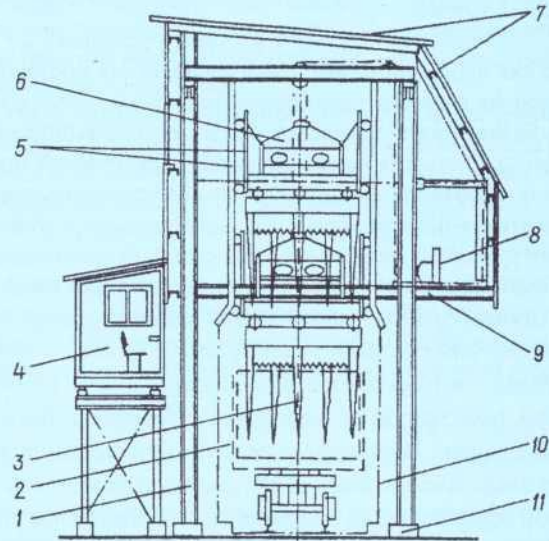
Общая схема виброрыхлительной установки: 1 — несущие балки; 2 — железнодорожный полувагон; 3 — рабочий орган с рыхлящими штырями; 4 — операторная; 5 — система направляющих; 6 — виброизоляционная траверса; 7 — перекрытие; 8 — лебедка; 9 — балка ярусного перекрытия; 10 — габарит подвижного состава; 11 — фундаменты.
